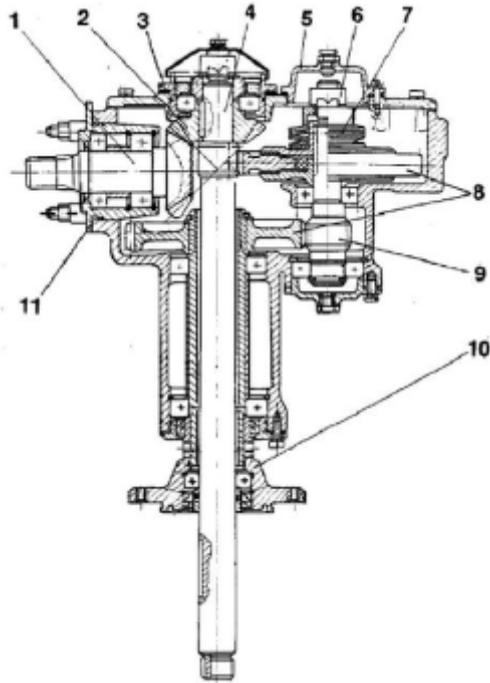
Цилиндрический редуктор: 1, 2 – конические шестерни;
